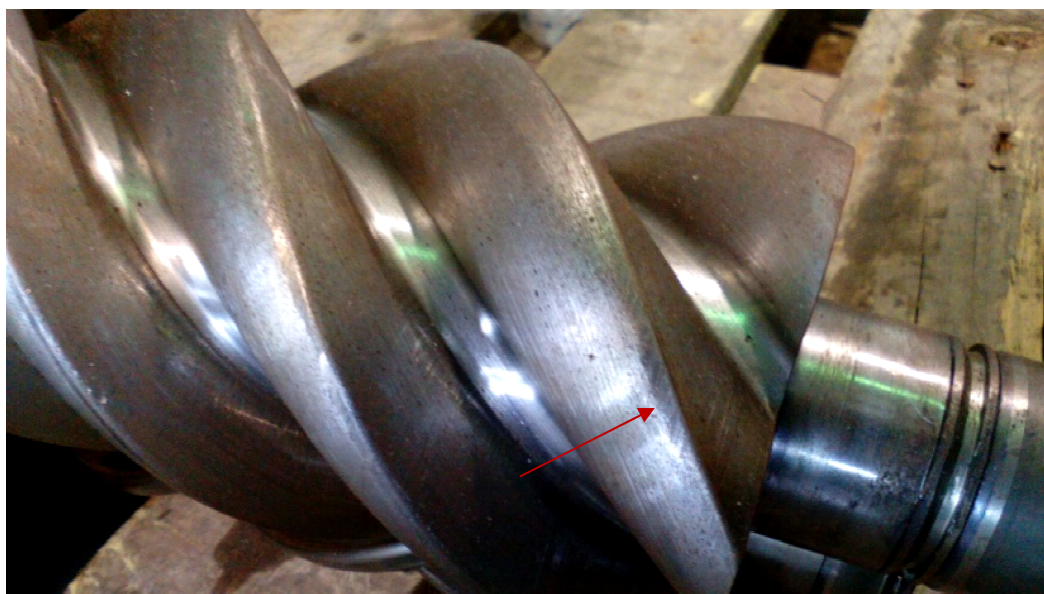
Rotor de elemento compressor com sinais de contacto metal-metal
